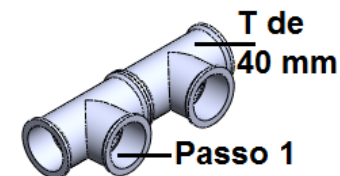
Montagem dos módulos – Módulo 6 – Passo 2
